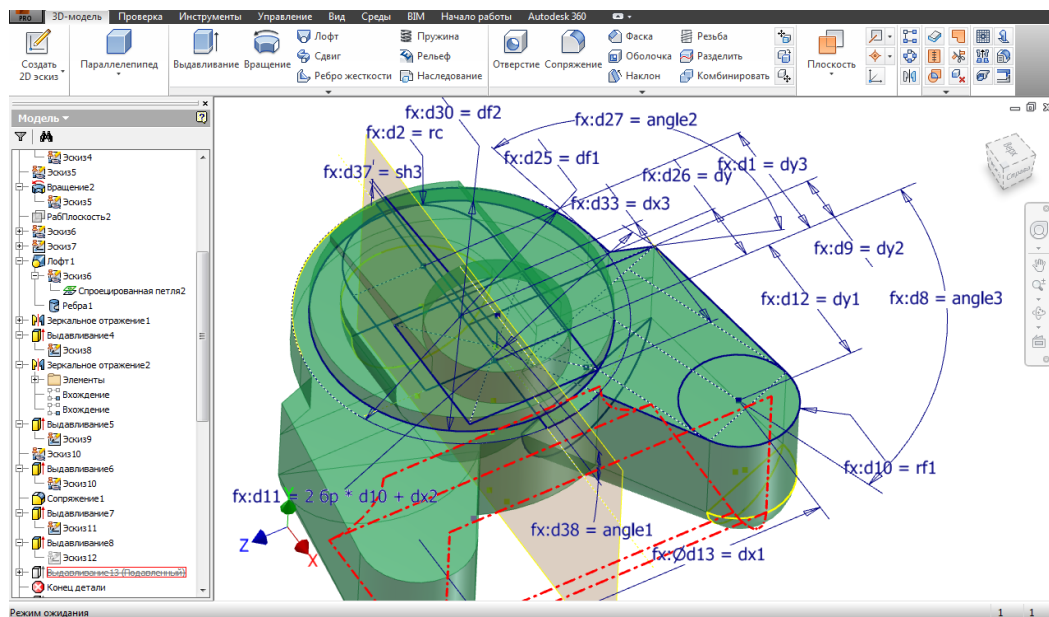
Модель базової частини корпусу гальмівного циліндра
